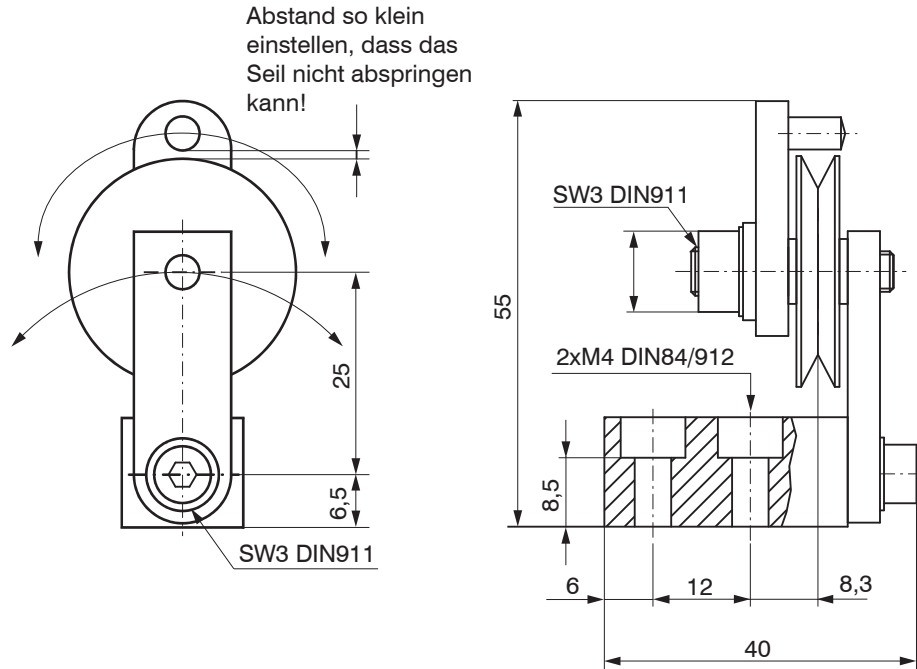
Umlenkrolle TR1-WDS mit Montagefuß, Abmessungen in mm
